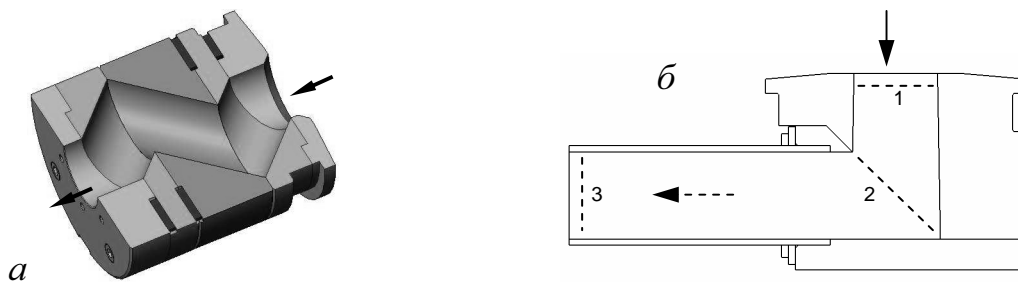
Инструмент для равноканального углового прессования с прямым (а) и боковым истечением (б)
